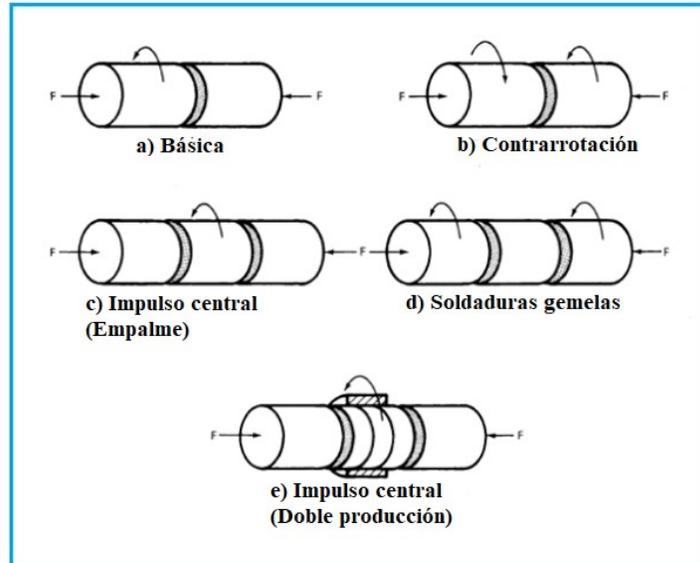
Etapas fundamentales de la soldadura por fricción rotativa.
